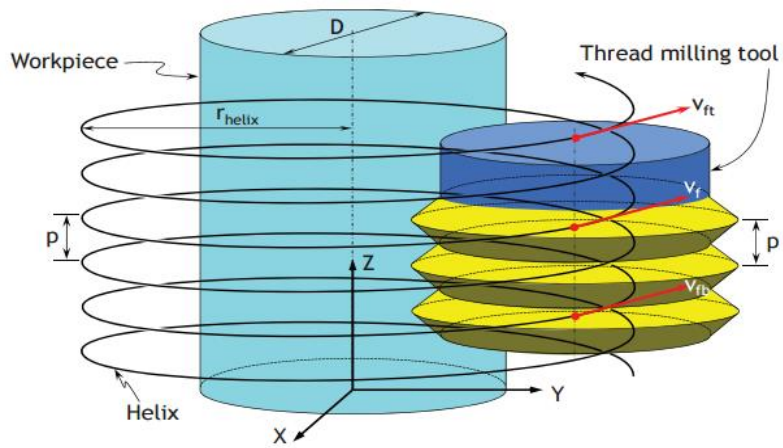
Відносне розміщення різьбової фрези та заготовки при нарізанні різьби [15]
